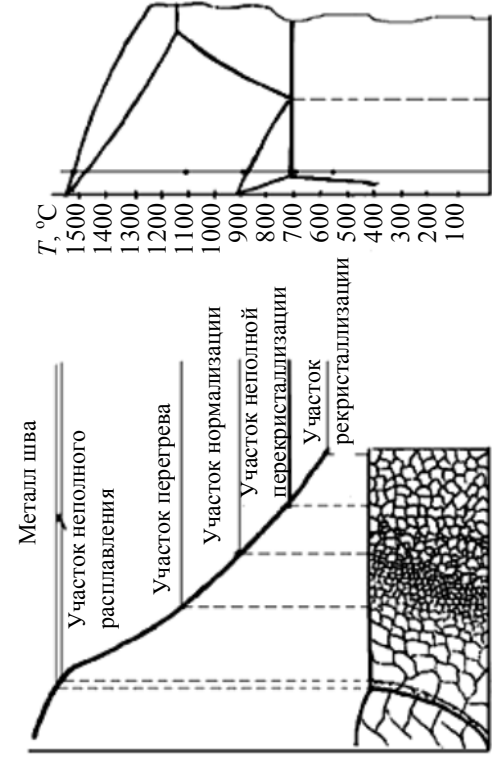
Строение ЗТВ при сварке низкоуглеродистой стали
